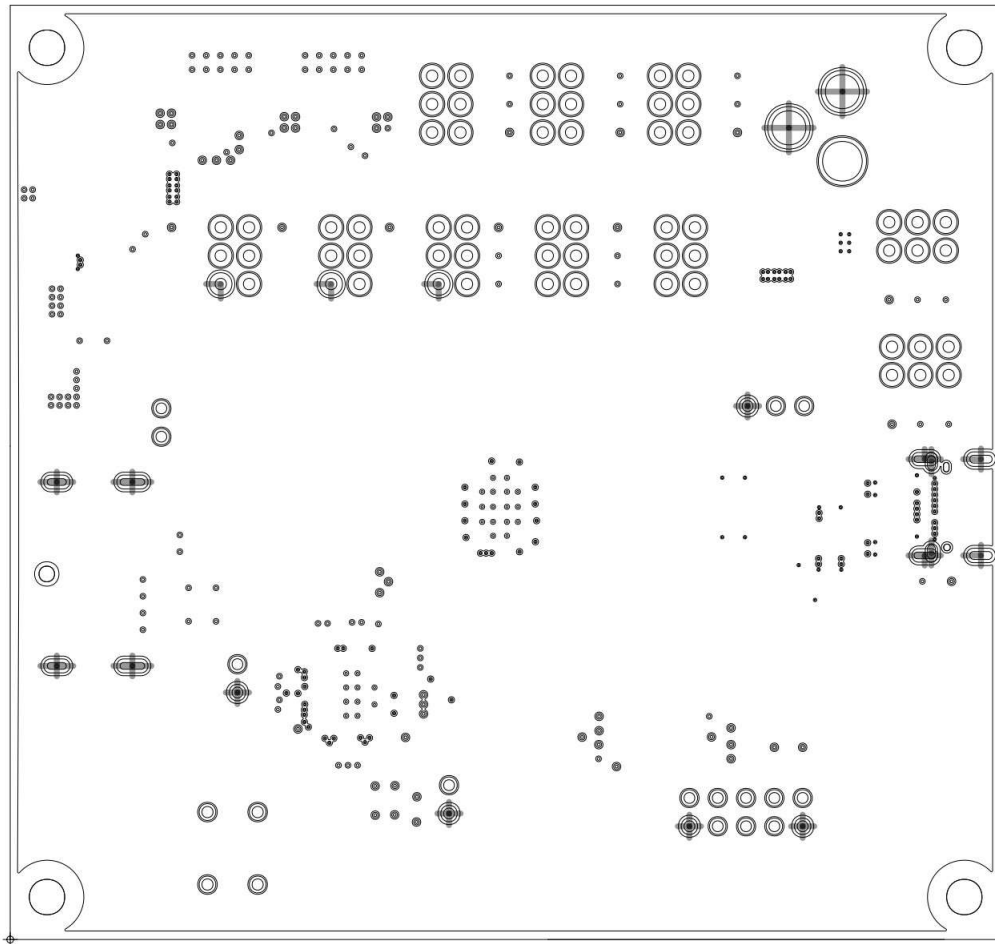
TUSB5461-Q1 EVM PCB 第 5 层 (GND)
